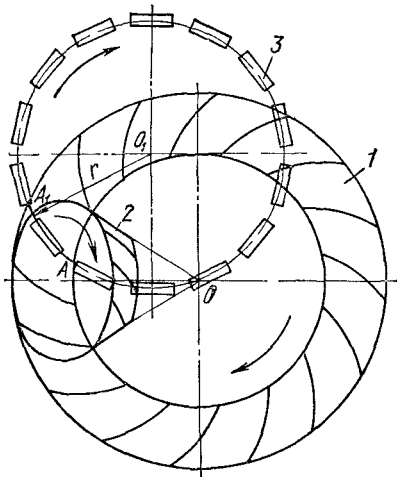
Схема нарезания конических колес с круговыми зубьями
